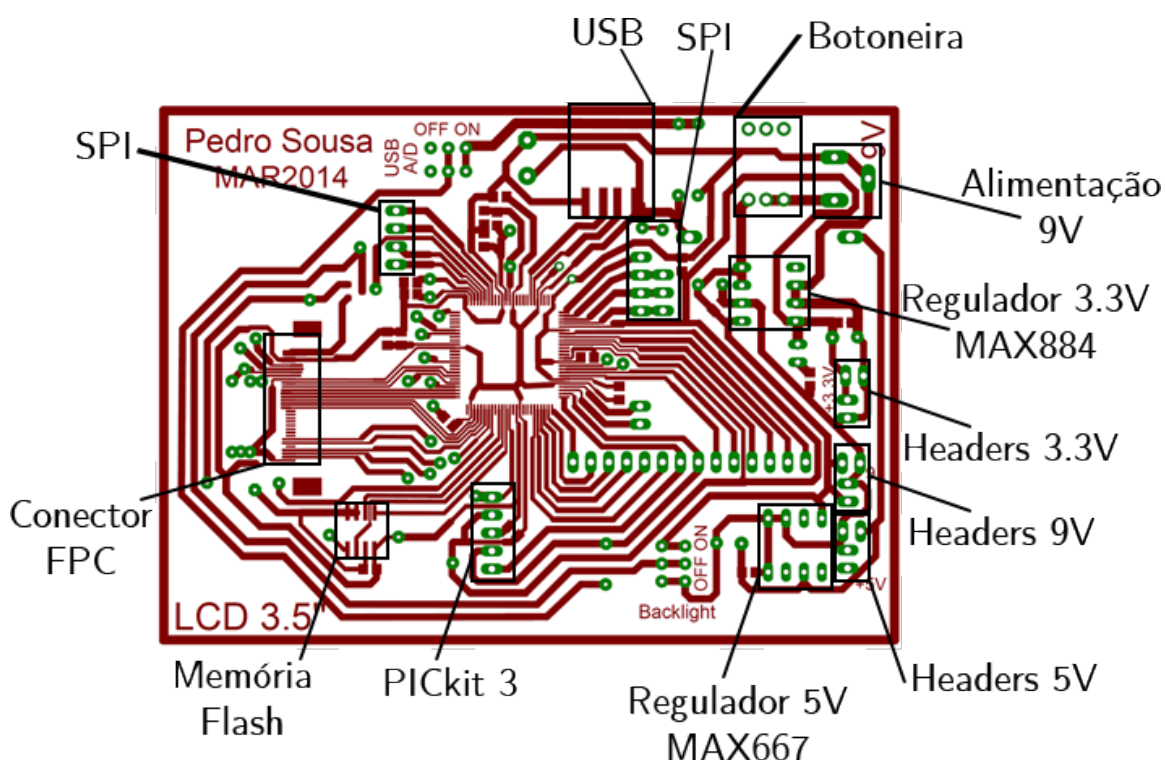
Placa de circuito impresso central, com indicação dos principais componentes
